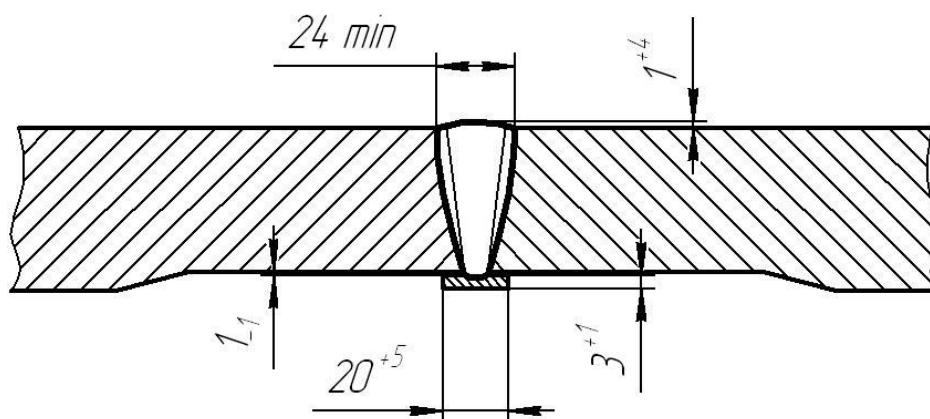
Внешний вид сварного соединения и требования к его геометрии
